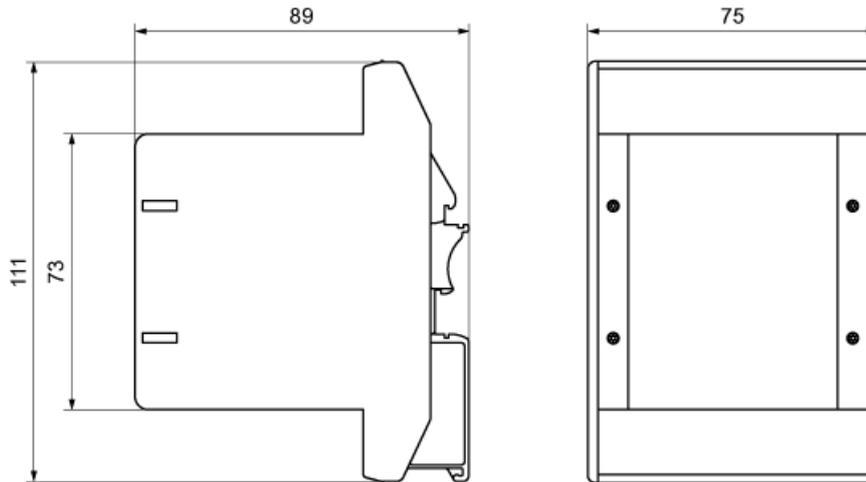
Disegno quotato Safe Brake Adapter (indicazioni in mm)
